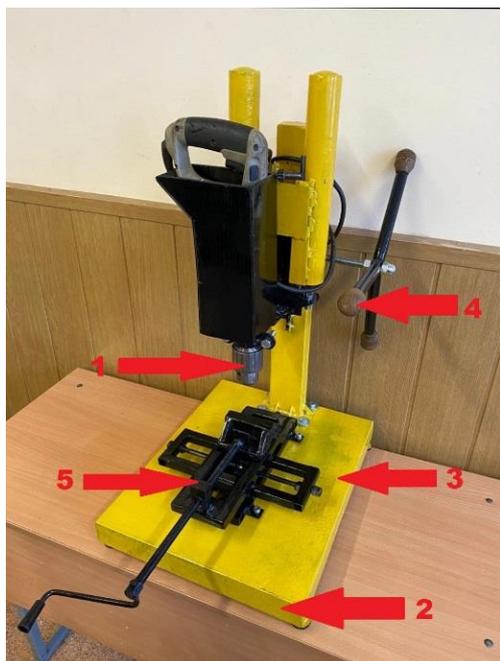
Внешний вид вертикально-сверлильного станка с координатными тисками: 1 - сверлильная головка; 2 - станина; 3 - рычаг подъема; 4 - рабочий стол; 5 - координатные тиски
